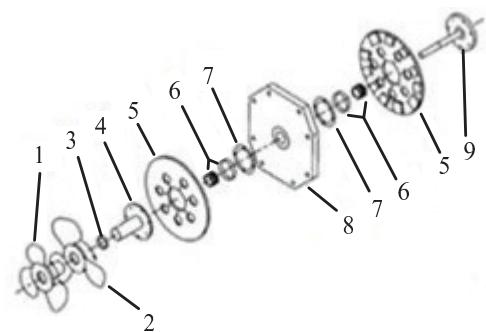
Разобранный вид дисковой машины с противовращающимся ротором: 1 – основной винт; 2 – противовращающийся винт; 3 – радиальный подшипник; 4 – внешний вал; 5 – ротор с ВПМ; 6 – подшипники; 7 – монтажное кольцо; 8 – статор; 9 – внутренний вал
